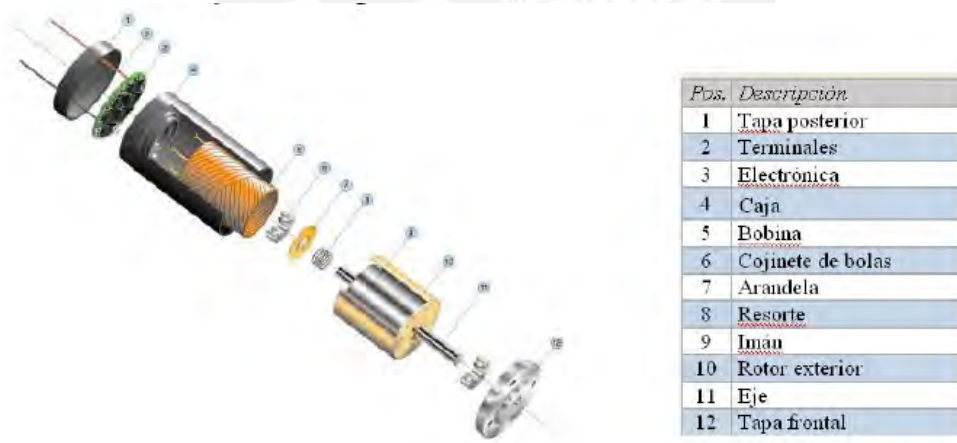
Componentes de un motor DC sin escobillas (brushless)²³
